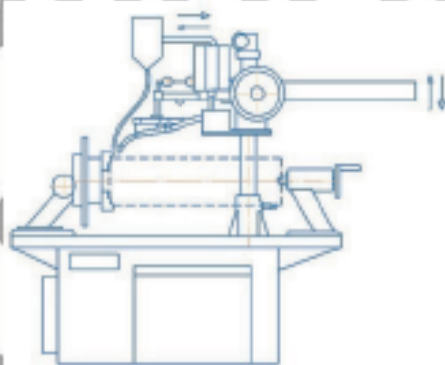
Загальний вигляд верстату для наплавлення
